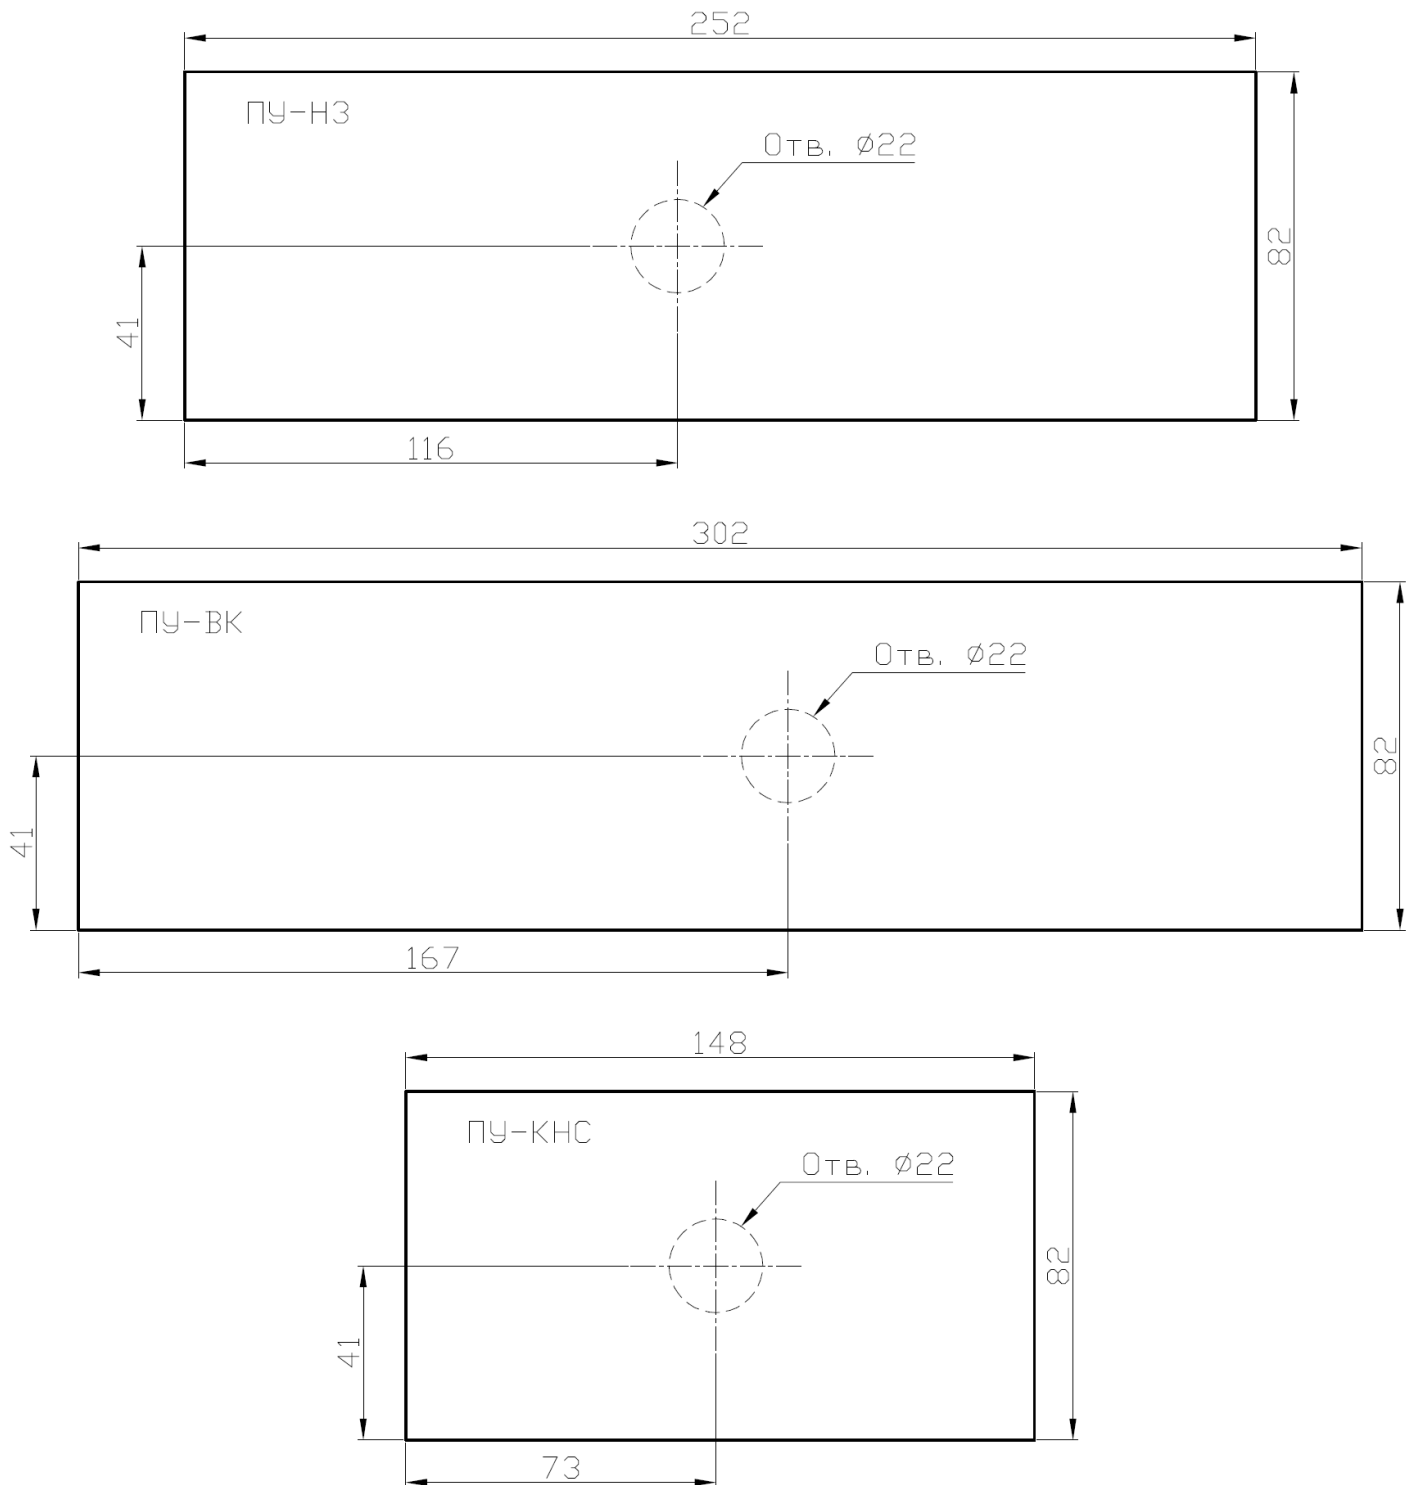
Габаритно-присоединительные размеры (вид с лицевой стороны)
